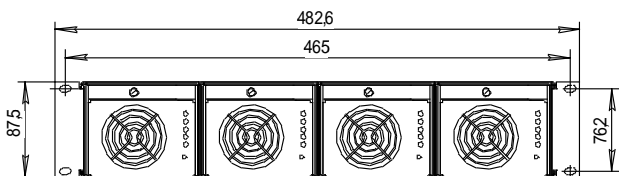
Габаритный чертеж УДЭП-2600
